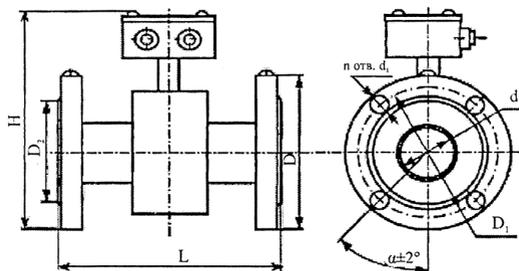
Габаритные и установочные размеры ПРПЭ типа ПРЭ.01
